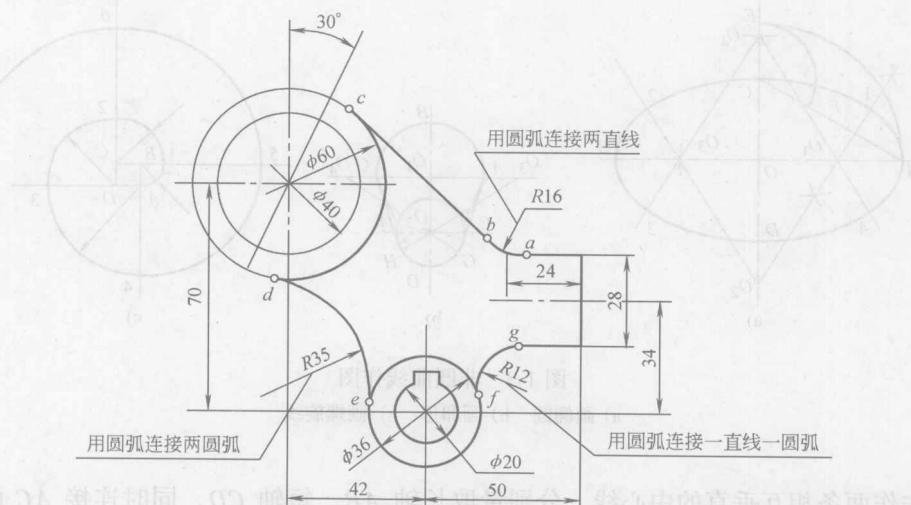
冲压件图样上的各种圆弧连接及尺寸标注
